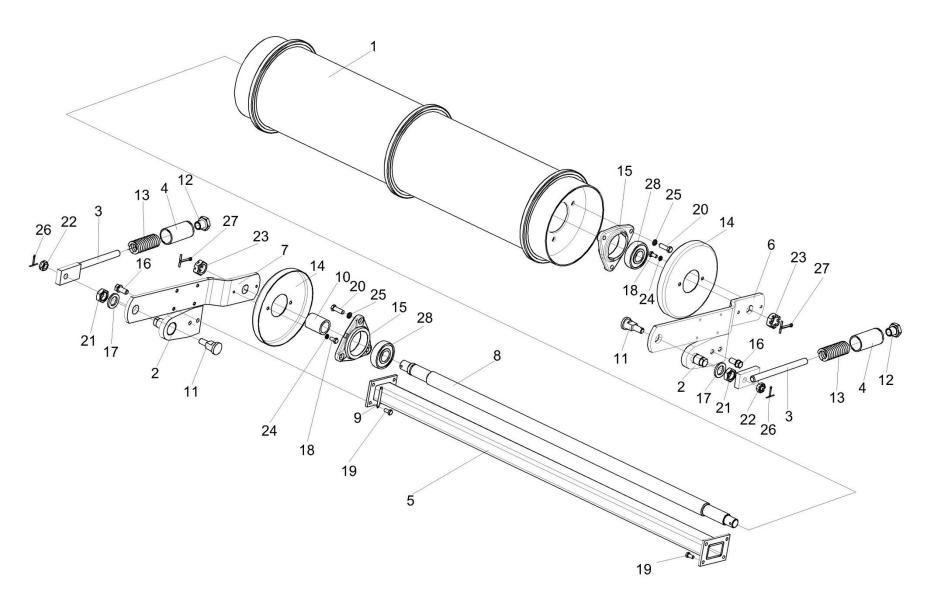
Установка вала нижнего КЗК-8-1816000
